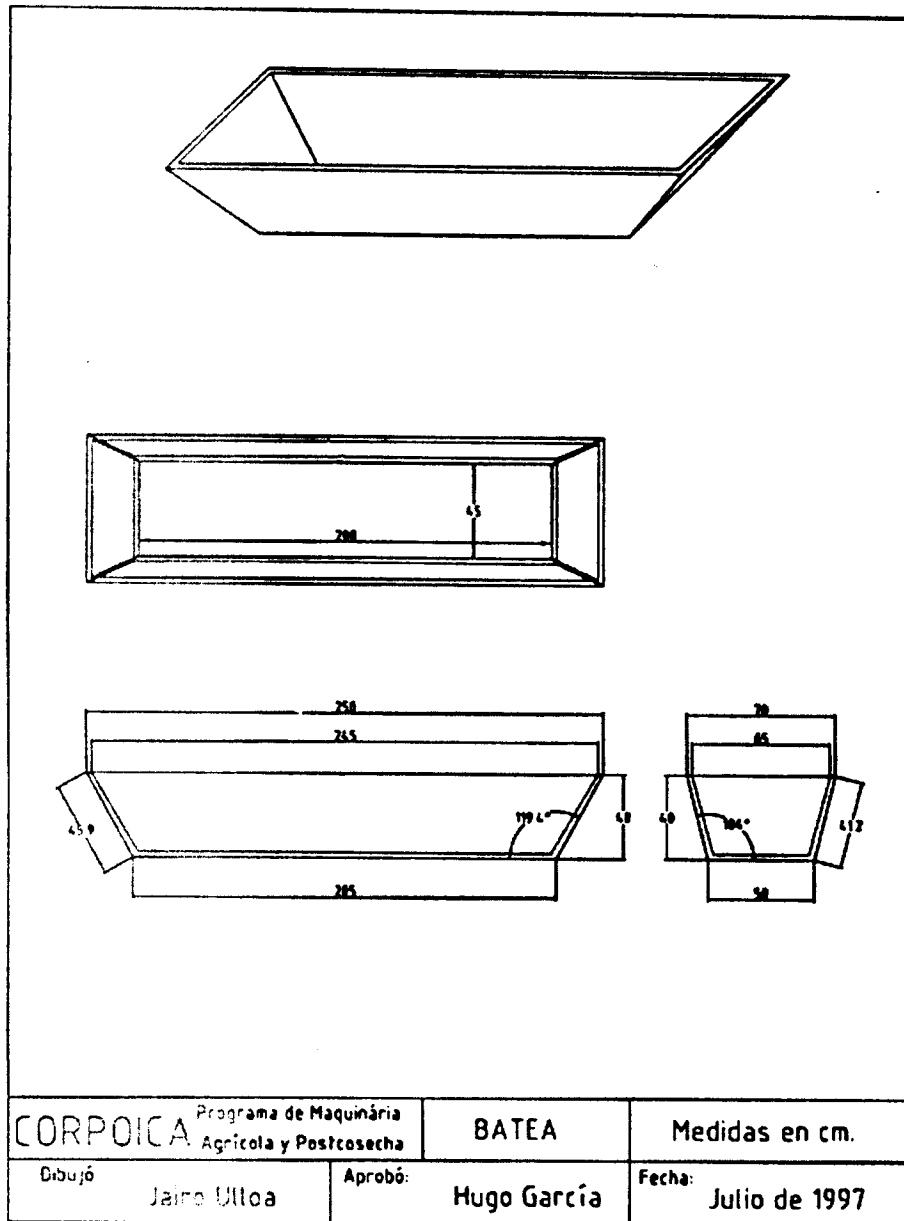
Plano de las bateas para sedimentación y lavado del almidón.
